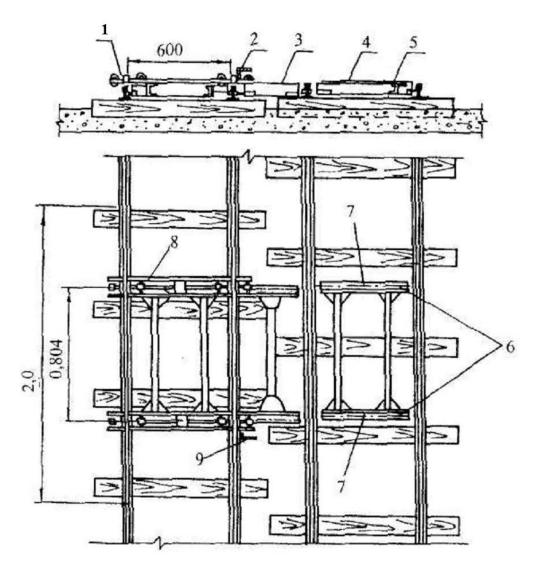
Конструкция платформы ППР-1 Условные обозначения: 1 – тележка; 2 – стопорное устройство; 3 – боковая рама; 4 – основная рама; 5 – неподвижный упор; 6 – направляющая рама; 7 – реборда; 8 – ролики; 9 – педаль
